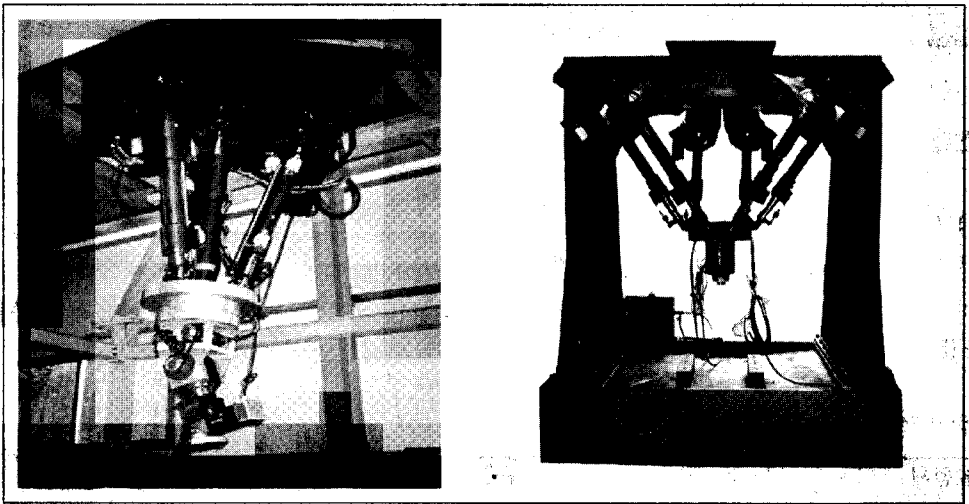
Propeller Blade Grinding Machine and 6 Axis Complex Shape Machine
